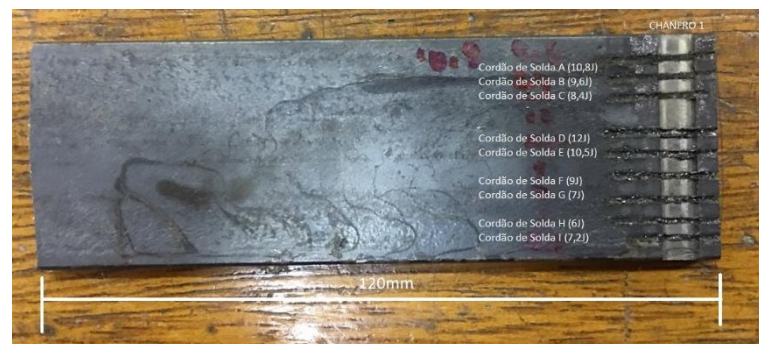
Chapa de Aço após soldagem [Elaborado pelo Autor].
